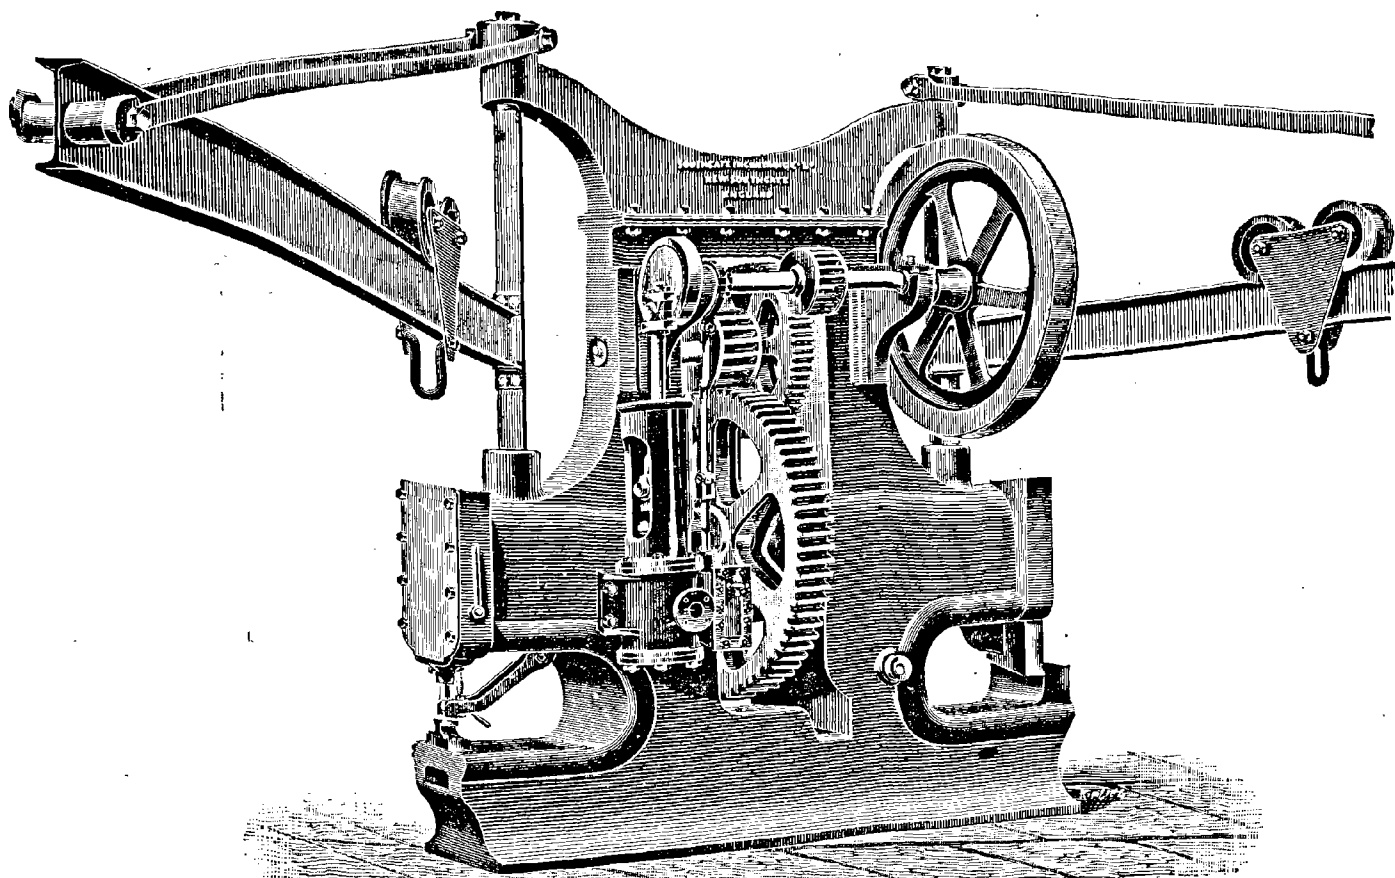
Machine double à poinçonner et cisailer de M. Lucas actionnée directement par une machine à vapeur montée sur le bâti.
